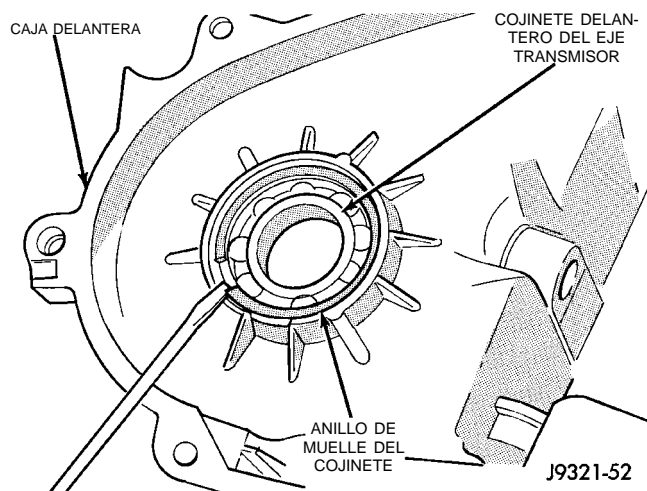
Desmontaje del anillo de muelle del cojinete delantero del eje transmisor
